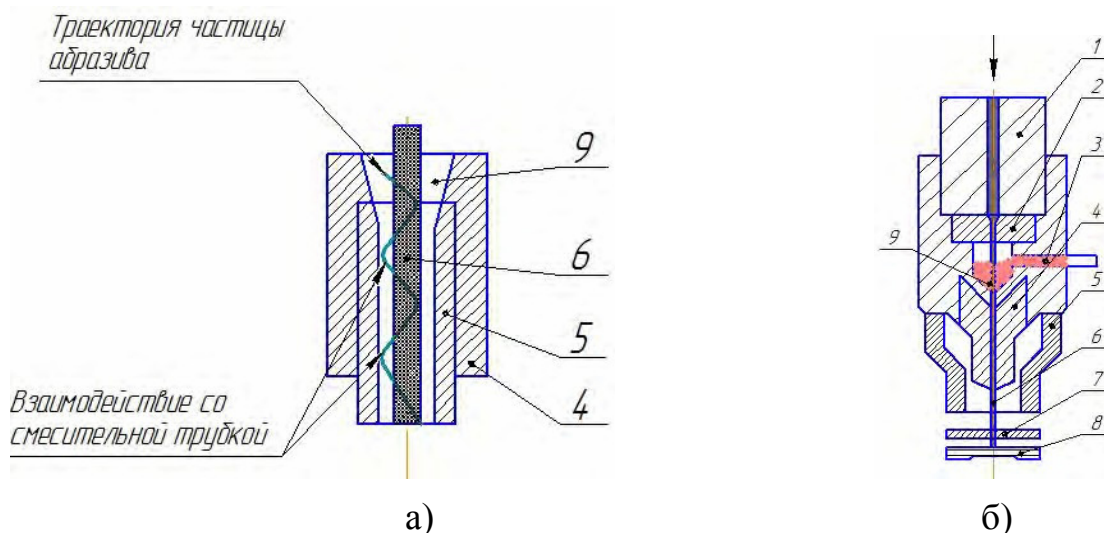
Схемы режущей головки (б) и траектории движения частиц в смесительной трубке (а): 1 – подводящий водовод; 2 – сопло; 3 – подвод абразива; 4 - смесительная трубка; 5 – кожух; 6 – режущая струя; 7 – разрезаемый материал; 8 – гасящий слой воды; 9 – смесительная камера
